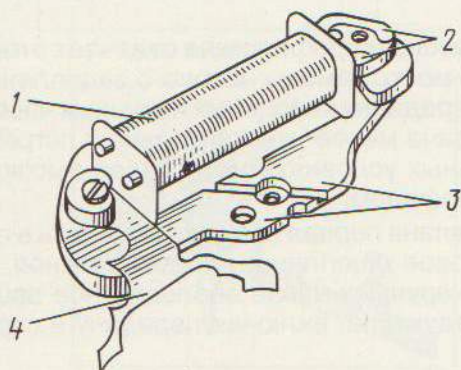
Статор шагового двигателя с вынесенной катушкой:
